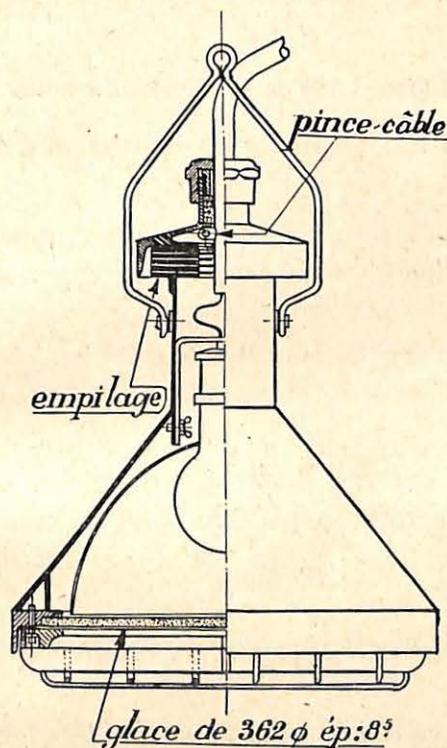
Armature des Charbonnages de Maurage pour lampe d'avalleresse.
